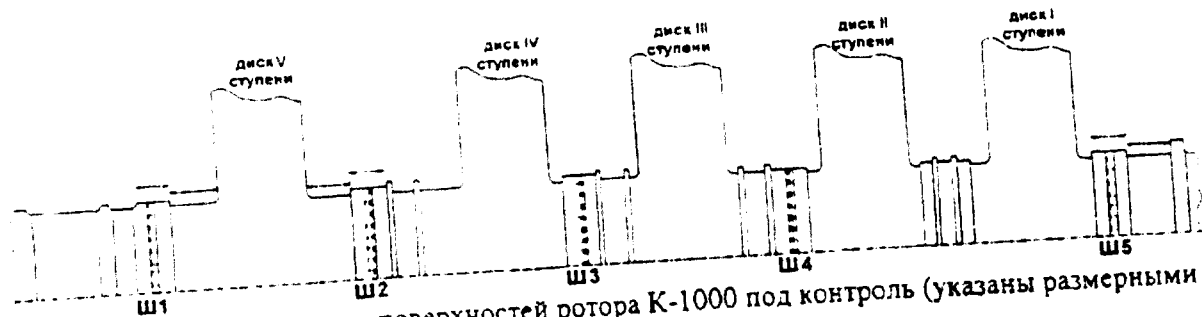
Места зачистки поверхностей ротора К-1000 под контроль (указаны размерными линиями)
